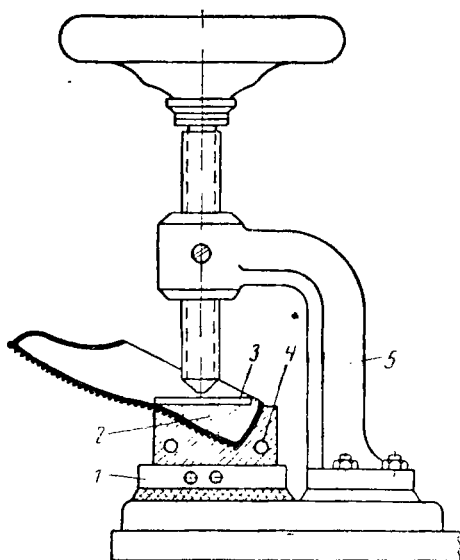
Запрессовка каблука галоши в раздвижной прессформе:
